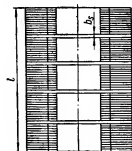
Эскиз активной стали статора СМ: 1 — шихтованный пакет статорного сердечника; 2 — межпакетный вентиляционный канал.
